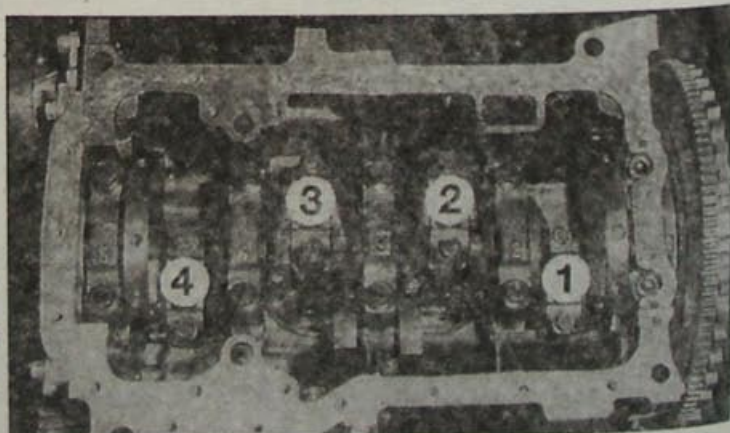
Установка упорных полуколец регулировки осевого люфта коленчатого вала
